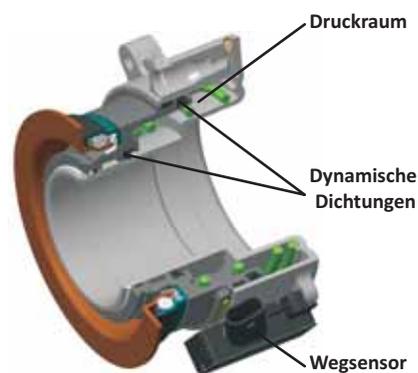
Gehäusefester Ausrücker für eine Hybridkupplung
